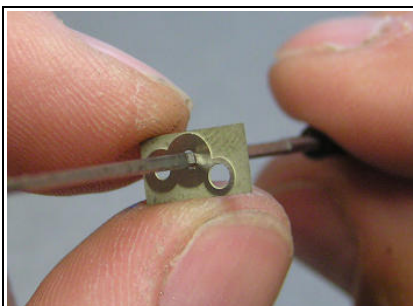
Das mittlere Loch auf 1,4mm (entspricht Buchsen-
